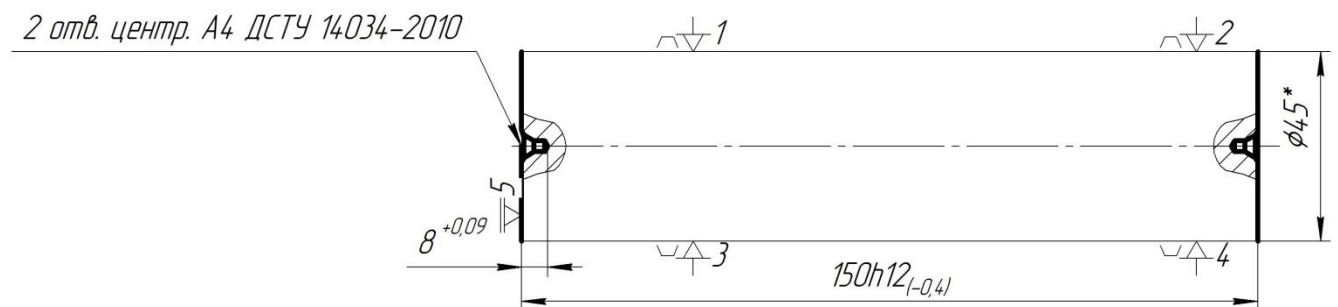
Схема установки заготовки в самоцентрувальні призми
